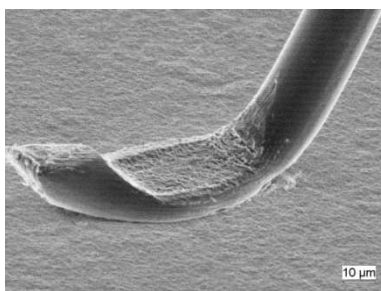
Внешний вид сварного соединения алюминиевой проволокой диаметром 30 мкм на частоте 120 кГц
